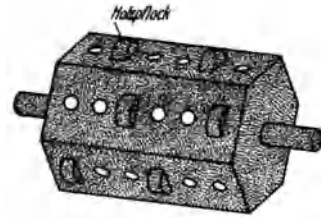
Steuerungszyylinder für Schafmaschinen wie in Abb. 551, jedoch mit einsetzbaren Holzpflocken als Anschlägen.
